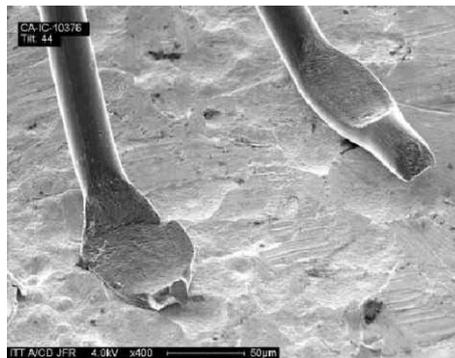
Фото сварного соединения клин (СЭМ)
